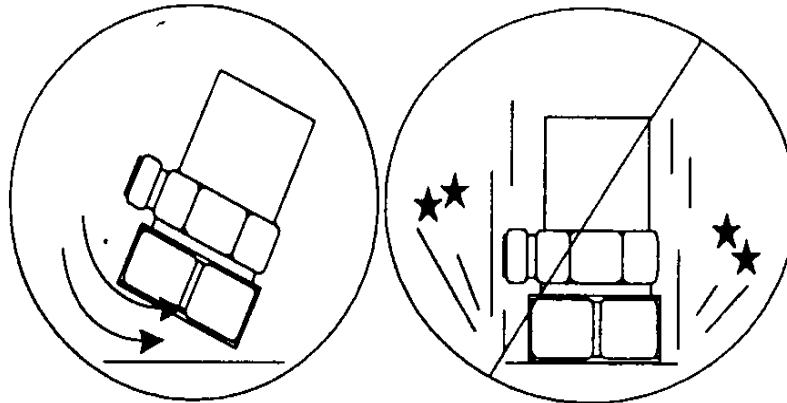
Установка сборки магнит-датчик на поверхность агрегата
